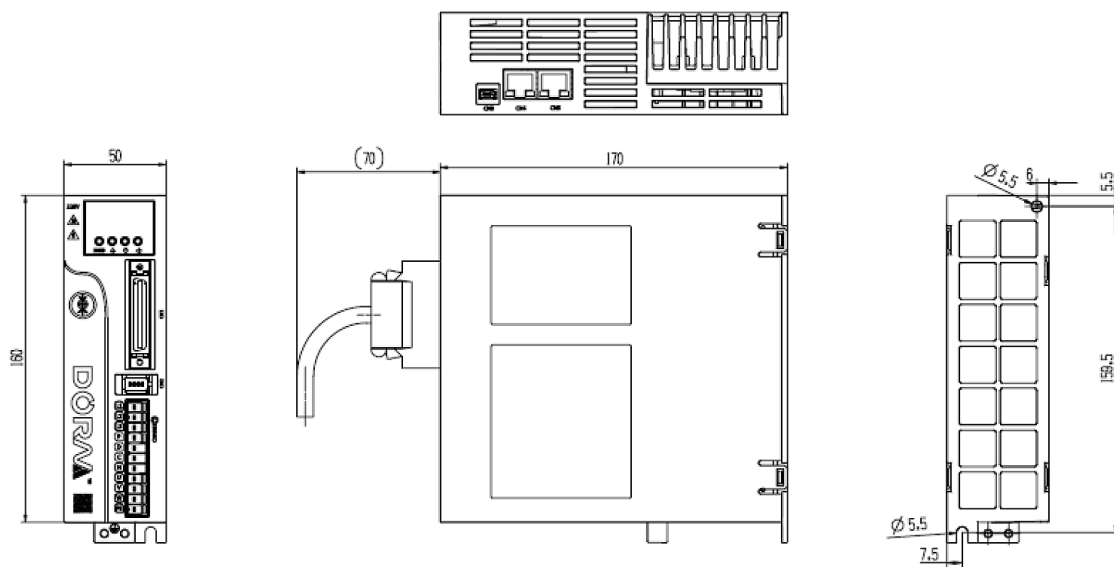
Габаритные размеры драйвера, тип корпуса А (220 В,  $\leq 0.75$  кВт)
